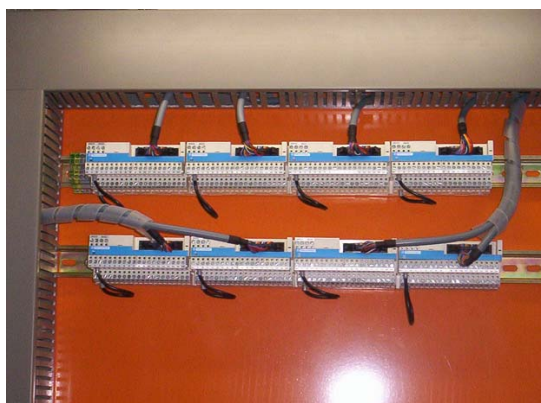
Montaje de borneras Telefast en Estación Elevadora.
